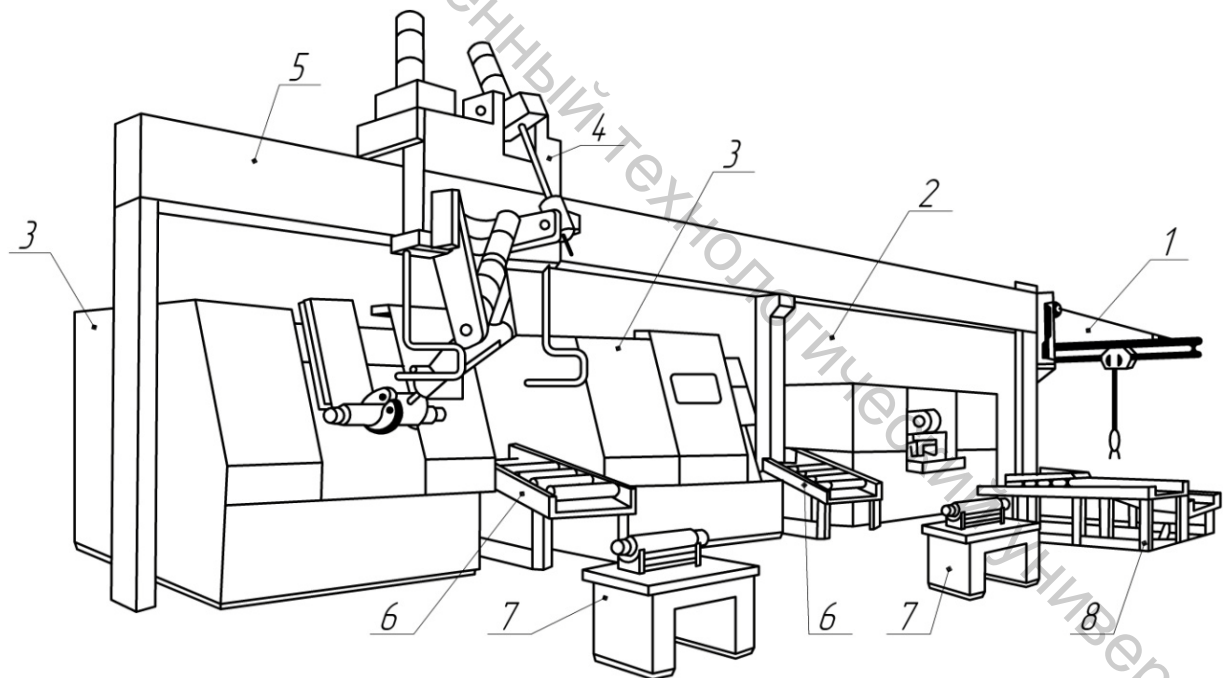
Автоматизированный участок обработки деталей типа тел вращения массой до 40 кг: 1 – поворотный кран; 2 – фрезерно-центровальный станок; 3 – токарные патронно-центровые станки с ЧПУ; 4 – подвижная каретка с рукой робота SM40Φ2.80.01; 5 – монорельс; 6 – промежуточные накопители, перестраиваемые для хранения валов и фланцев; 7 – контрольные позиции; 8 – двухручьевого рольганг
